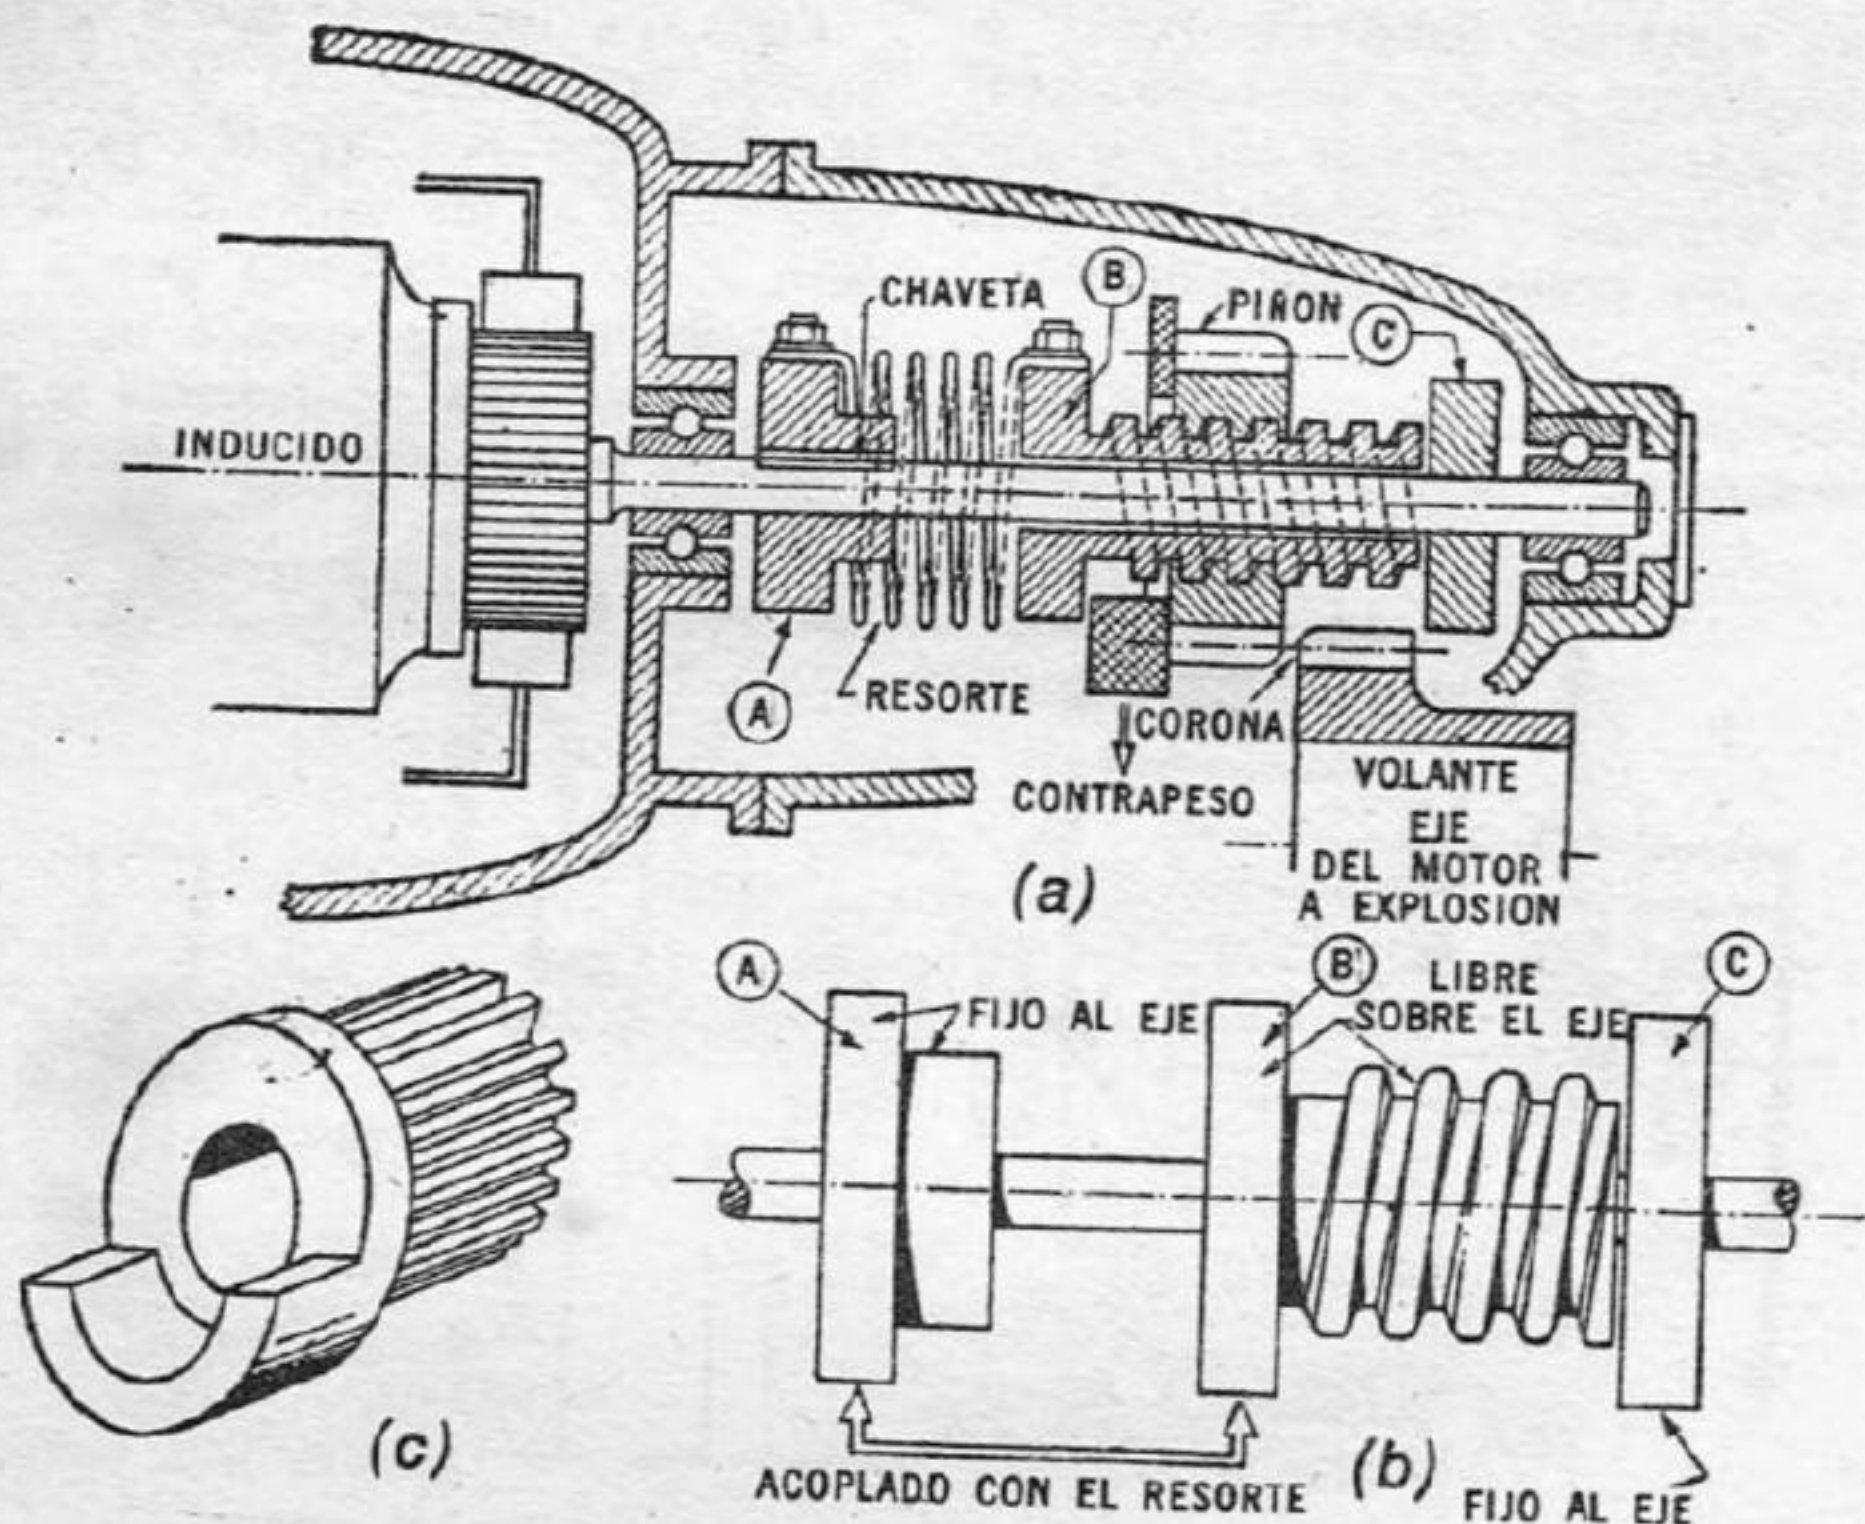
Conjunto de acoplamiento Bendix. Es el sistema adoptado universalmente.
